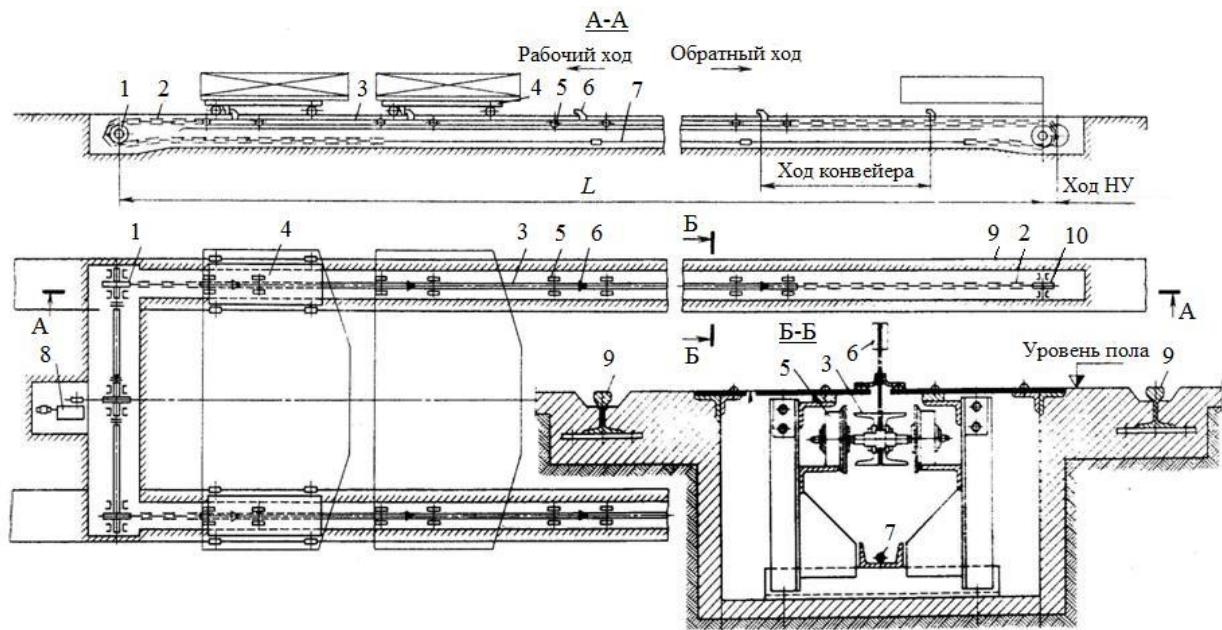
Схема грузоведущего двухштангового конвейера:
